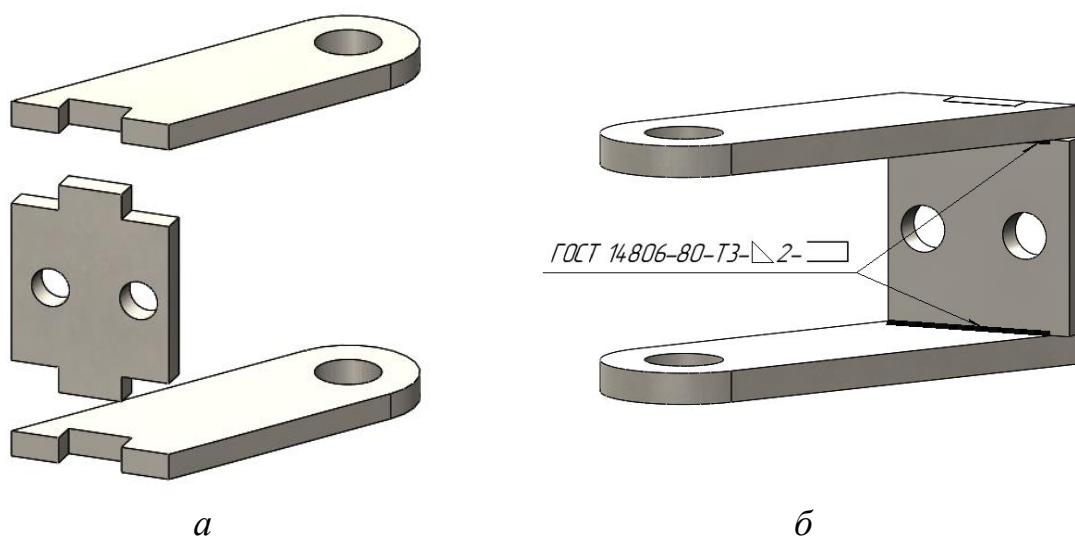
Сборка кронштейна крепления рулевых тяг: *а* – общий вид сборки; *б* – сварное соединение деталей.
